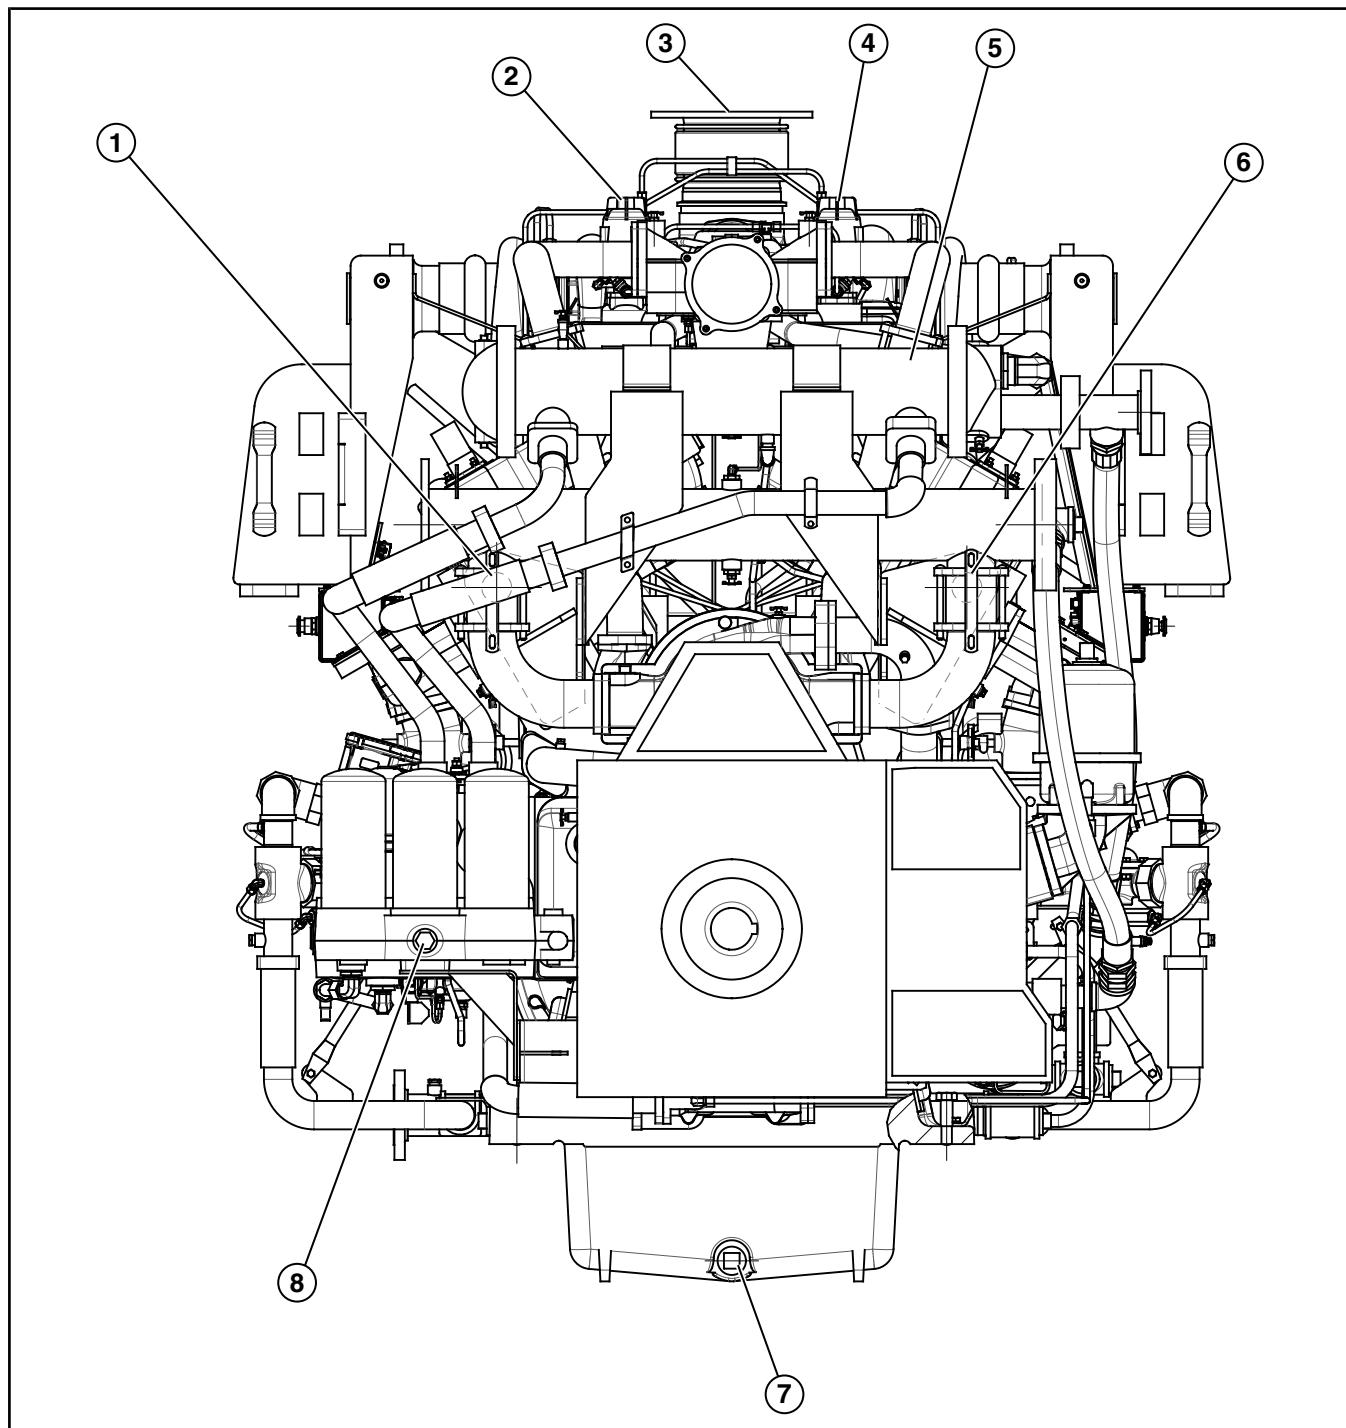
Вид спереди (двигатель L7044GSI)
